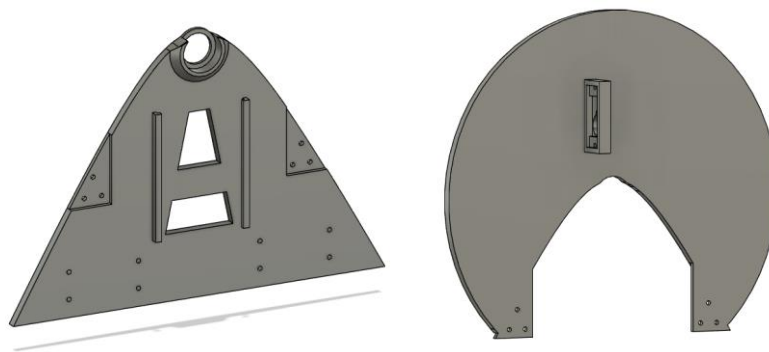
Subestructuras delantera (Planos 6/15 y 7/15)
